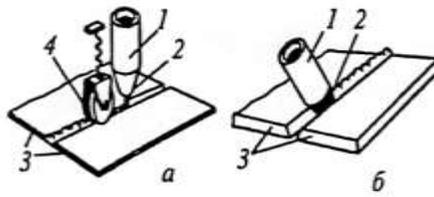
Схема бесконтактной (а) и контактной (б) экструзионной сварки расплавом: 1 – экструдер; 2 – мундштук экструдера; 3 – свариваемые детали; 4 – прокатывающий ролик
